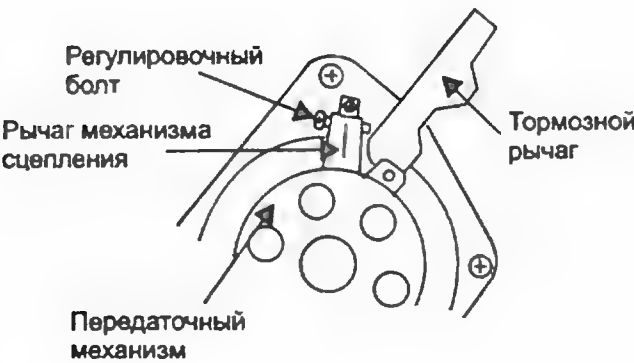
Регулировка механизма торможения (тормозной рычаг)
